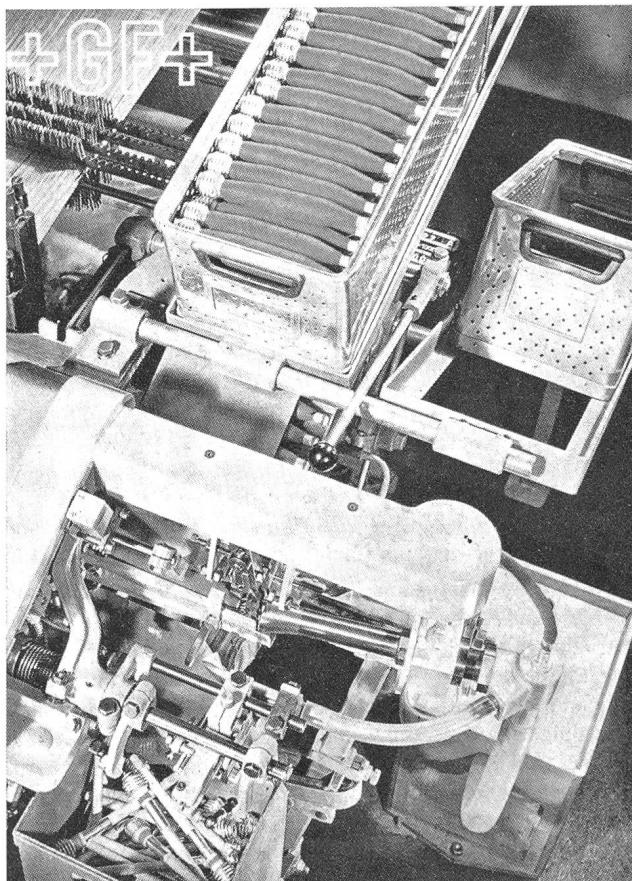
Kastenlader für Webautomat (+GF+ Brugg)
